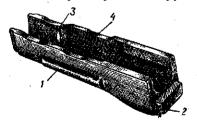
Цевье: 7 — упоры для пальцев; 2 — выступ; 3 — металлическая прокладка; 4 — вырезы
